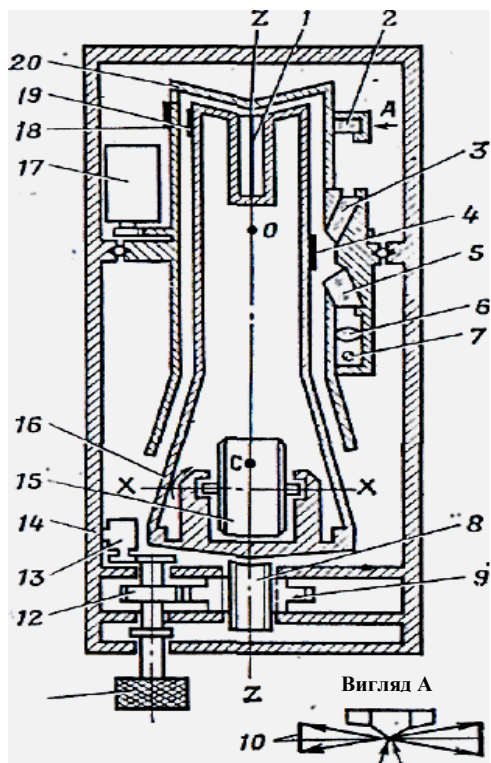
Принципова схема гіровузла гірокомпаса 1Г17: 1 – торсіон; 2 – роздільна призма; 3, 5 – призми; 4 – дзеркало; 6 – лінза; 7 – лампа; 8 – аретир; 9 – нарізна втулка; 10 – фотоопір; 11 – маховичок; 12 – шестірня; 13 – двигун автоматичного аретування; 14 – зовнішній корпус; 15 – гіромотор; 16 – чутливий елемент; 17 – двигун із редуктором; 18, 19 – автоколімаційні дзеркала чутливого елемента і слідкувального корпусу; 20 – слідкувальний корпус
